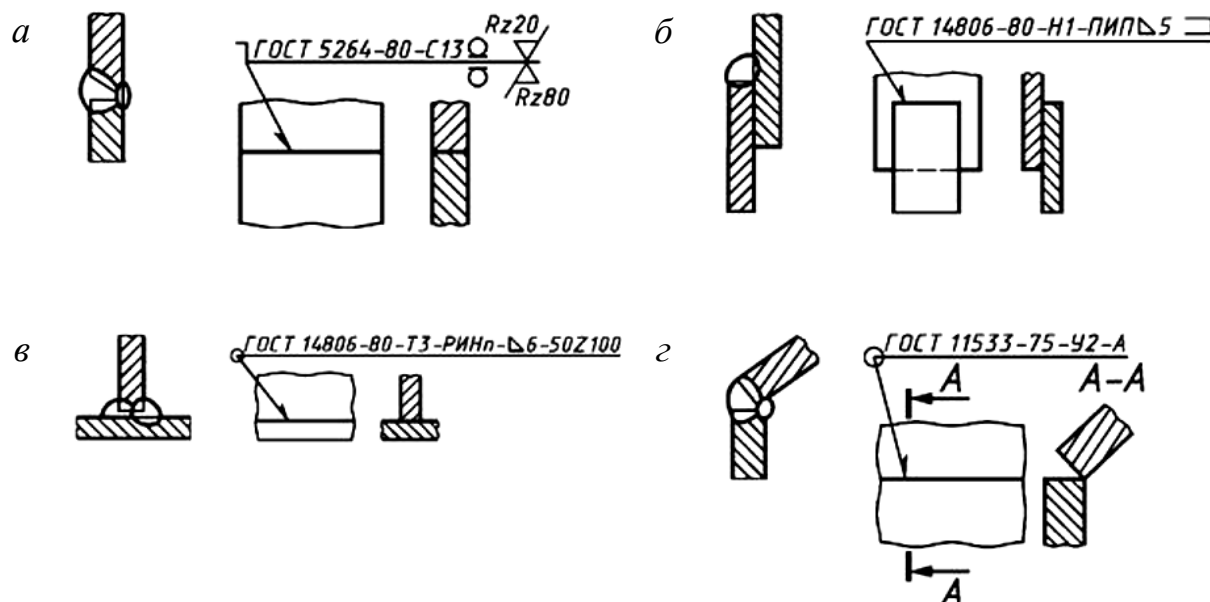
Примеры условных обозначений стандартных швов сварных соединений
